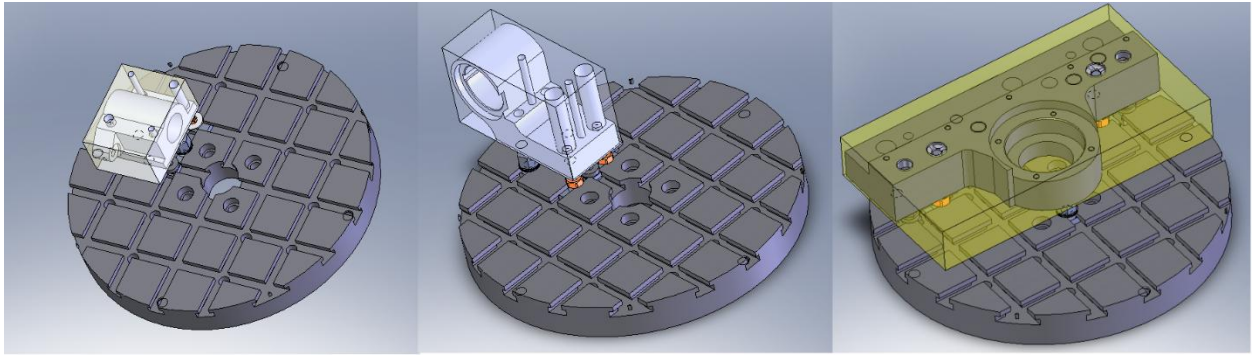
УЗП для обробки деталей типу «Кронштейн».
